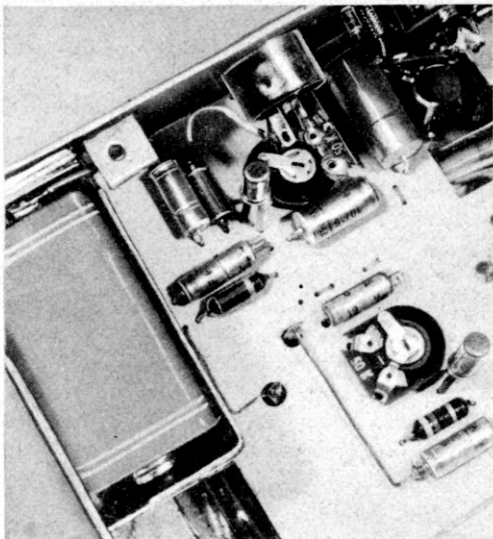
Ausschnitte und Bohrungen auf der Chassisrückseite
